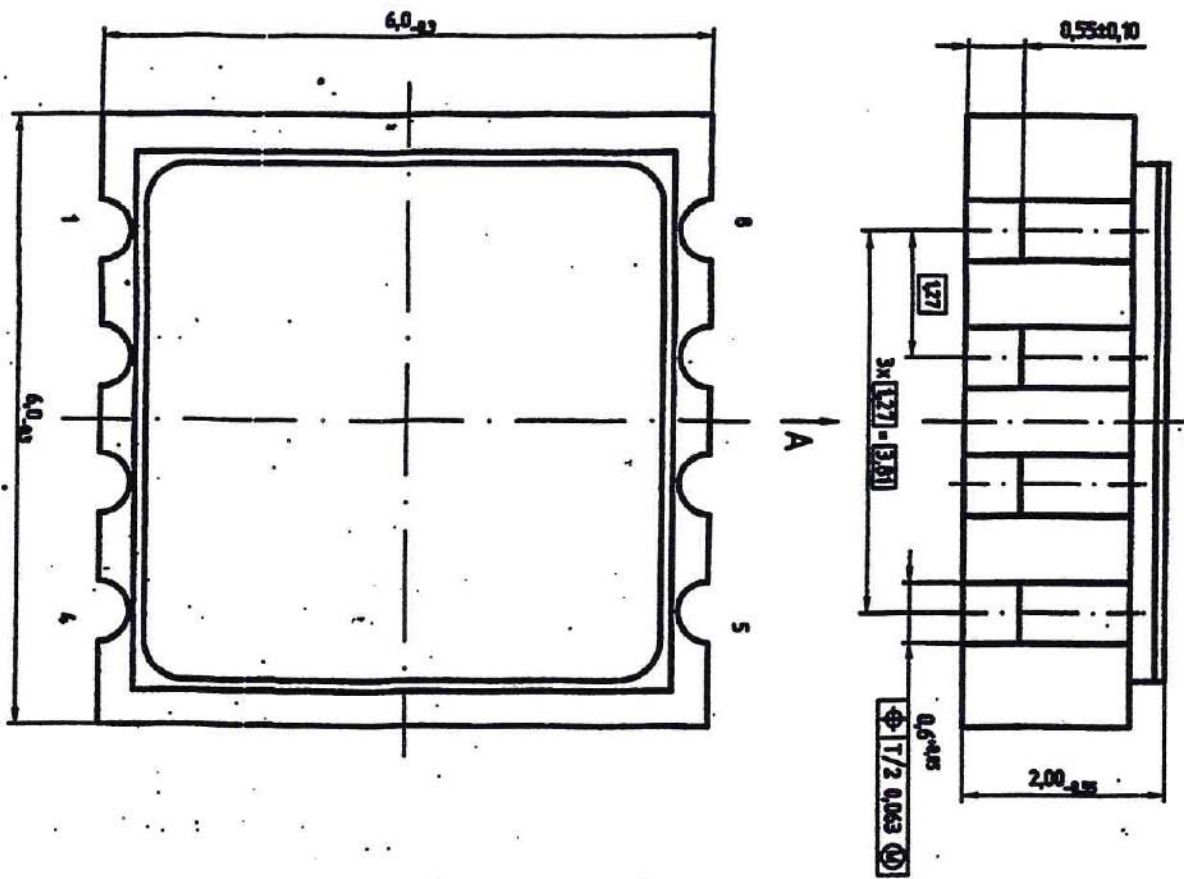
Габаритный чертеж корпуса 5205.8-2
